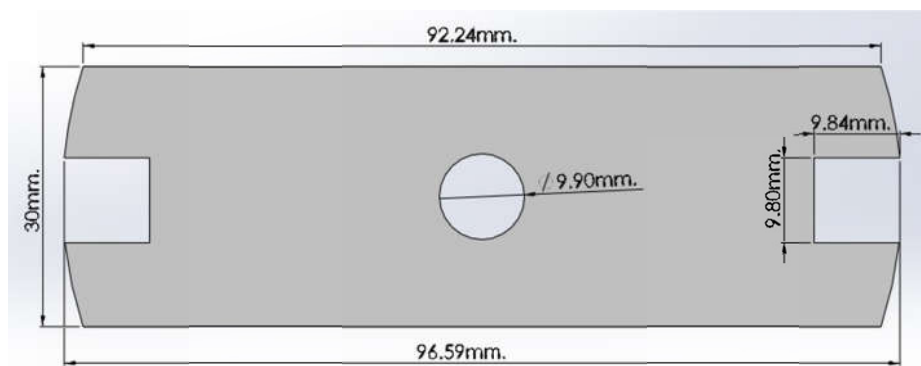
Pieza 3 del soporte para introducir las bobinas y la punta de prueba al magnetómetro.
